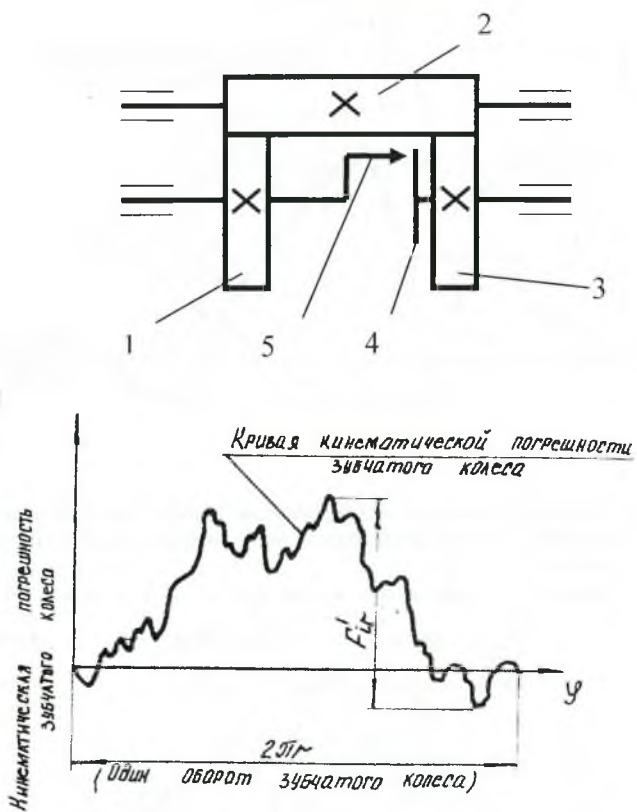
Схема установки и график кинематической погрешности зубчатого колеса: 1 - контролируемое колесо; 2,3 - эталонные колеса; 4 - диск с градусной шкалой; 5-стрелка; F'_{gr} - наибольшая кинематическая погрешность зубчатого колеса.
